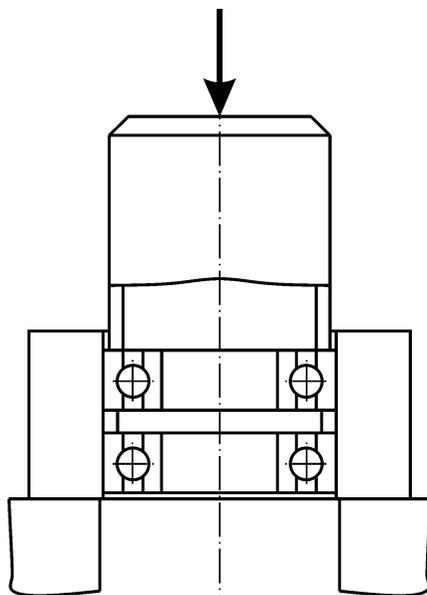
Разборка подшипников, установленных с натягом в корпусе
